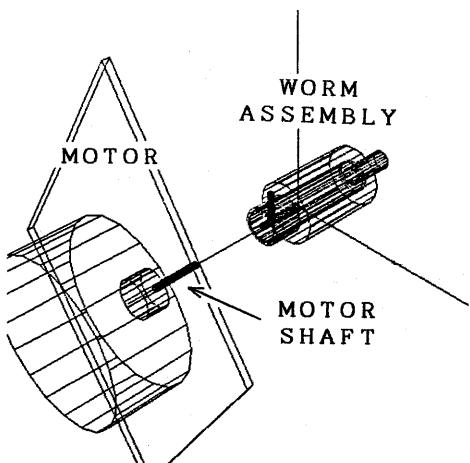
WORM ASSEMBLY と MOTOR SHAFT との軸合せ
